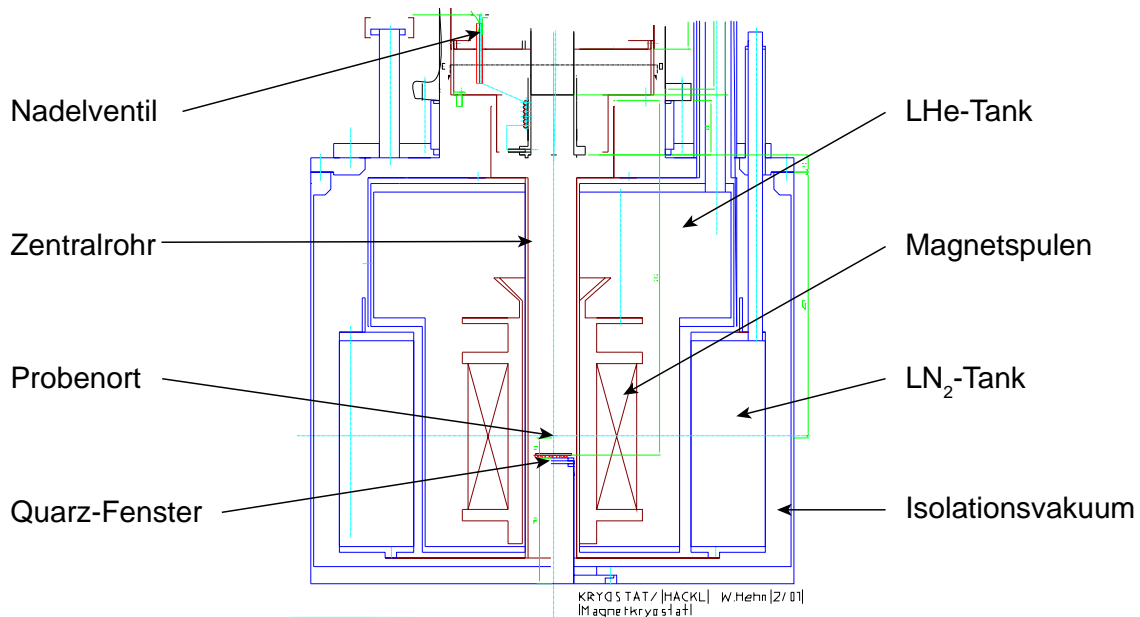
Ausschnitt der technischen Zeichnung des Magnetkryostaten. Wichtige Komponenten sind markiert und beschriftet. Die vollständige Zeichnung befindet sich im Anhang A.2.
